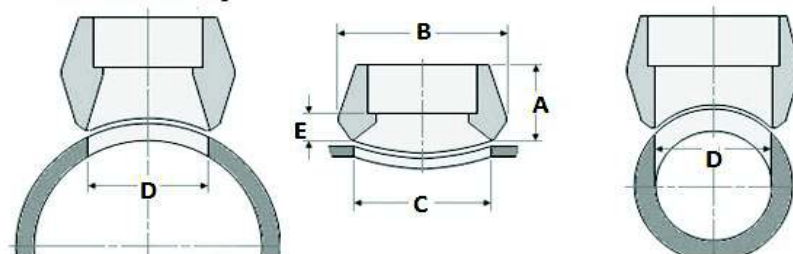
Dimensiones del elemento soldable (Theadolet).
